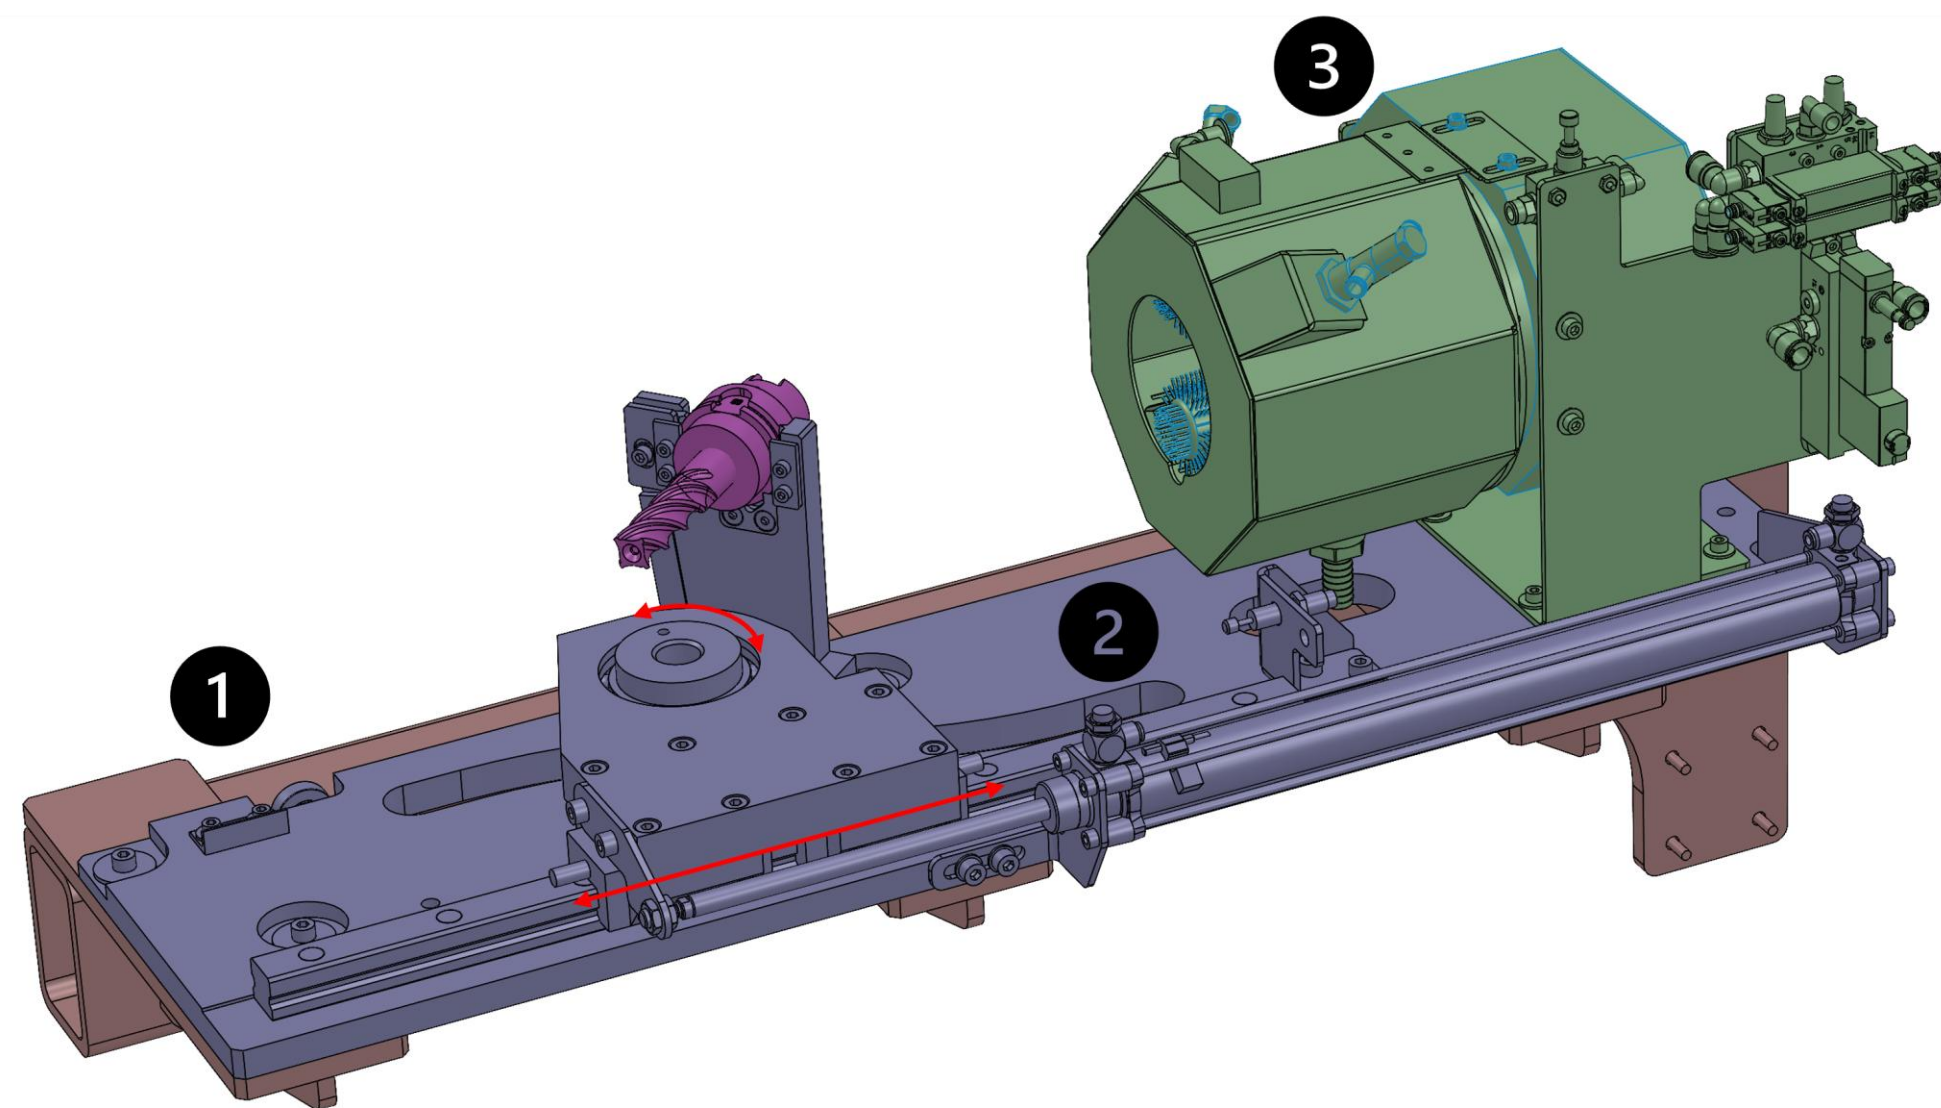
Frontansicht: Wird auf dem Hauptträger (1) montiert. Der Linearantrieb (2) fasst das Werkzeug und erzeugt die Schwenk-Hub-Bewegung, die das Werkzeug zur Reinigungsstation (3) bewegt.
